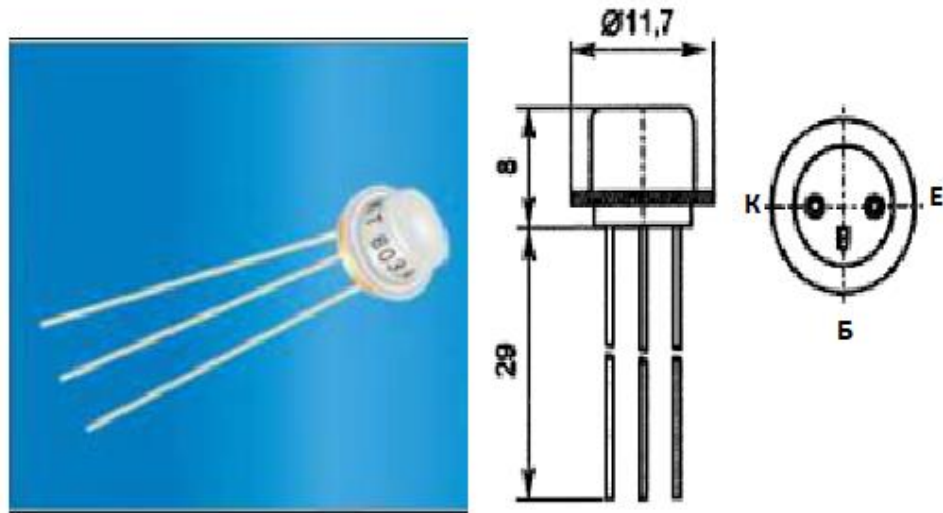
Зовнішній вигляд і цоколівка КТ603
